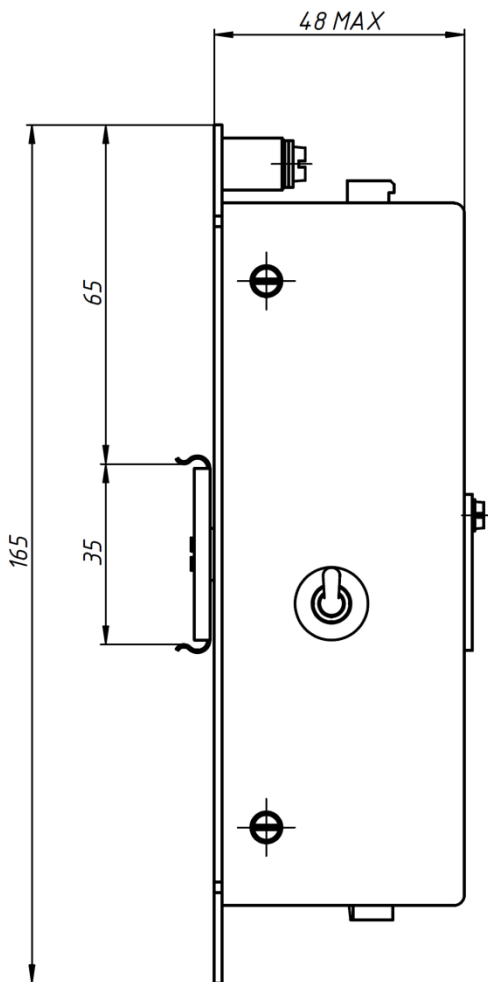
А. Внешний вид устройства «Орион-ДЗ» с креплением на DIN-рейку, верхний ввод.
